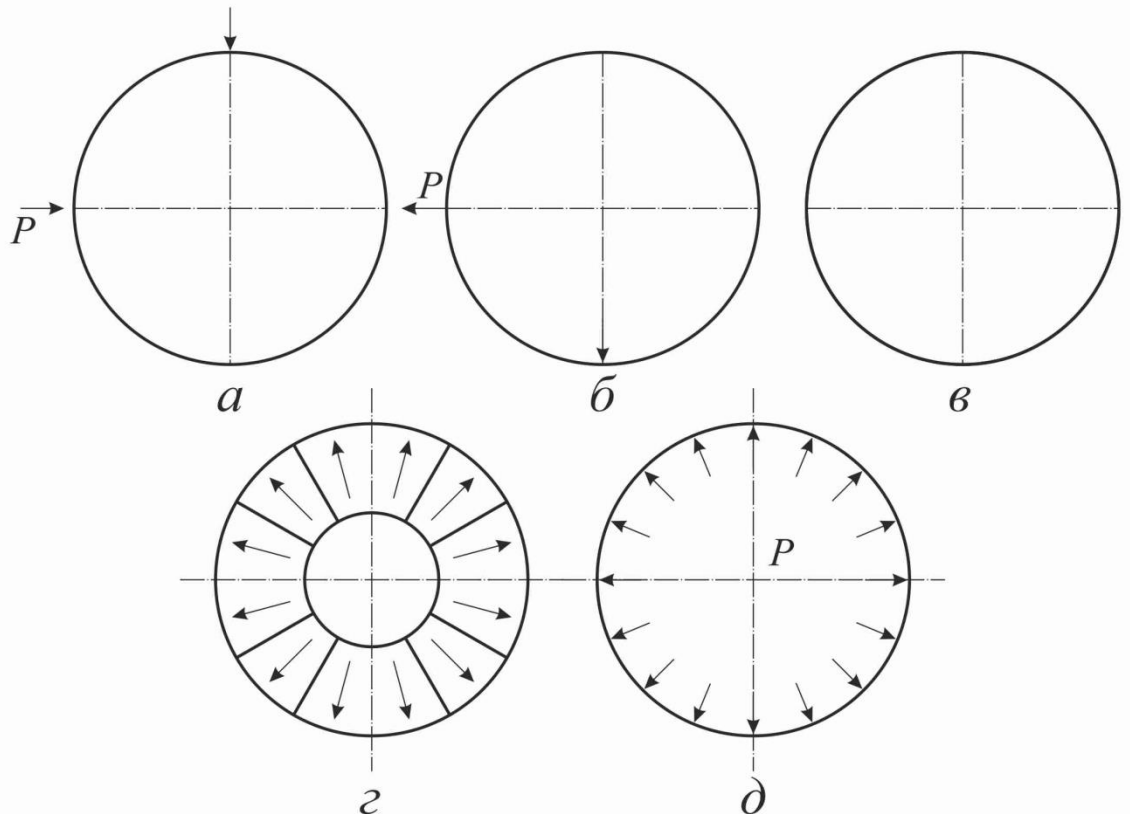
Схемы изготовления трубы: а - стыковка усилиями P и нанесение сборочного шва; б - четырехдуговая сварка внутренней части
